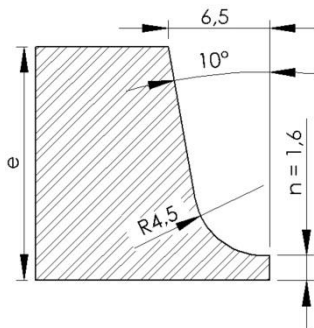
Chanfro tipo “U” utilizado por Sartori [17] para a execução de um procedimento de soldagem MIG/MAG mecanizada. Dimensões em mm.
